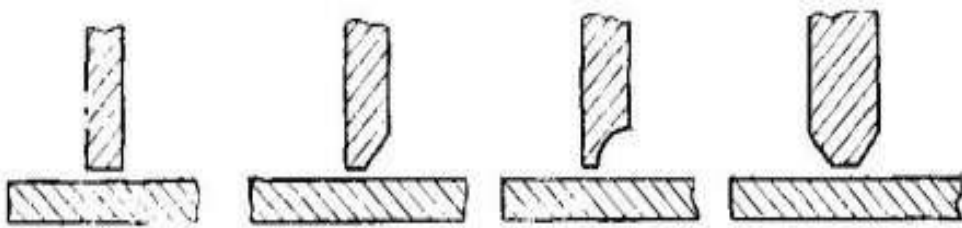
Форма подготовленных кромок под сварку для тавровых соединений.
